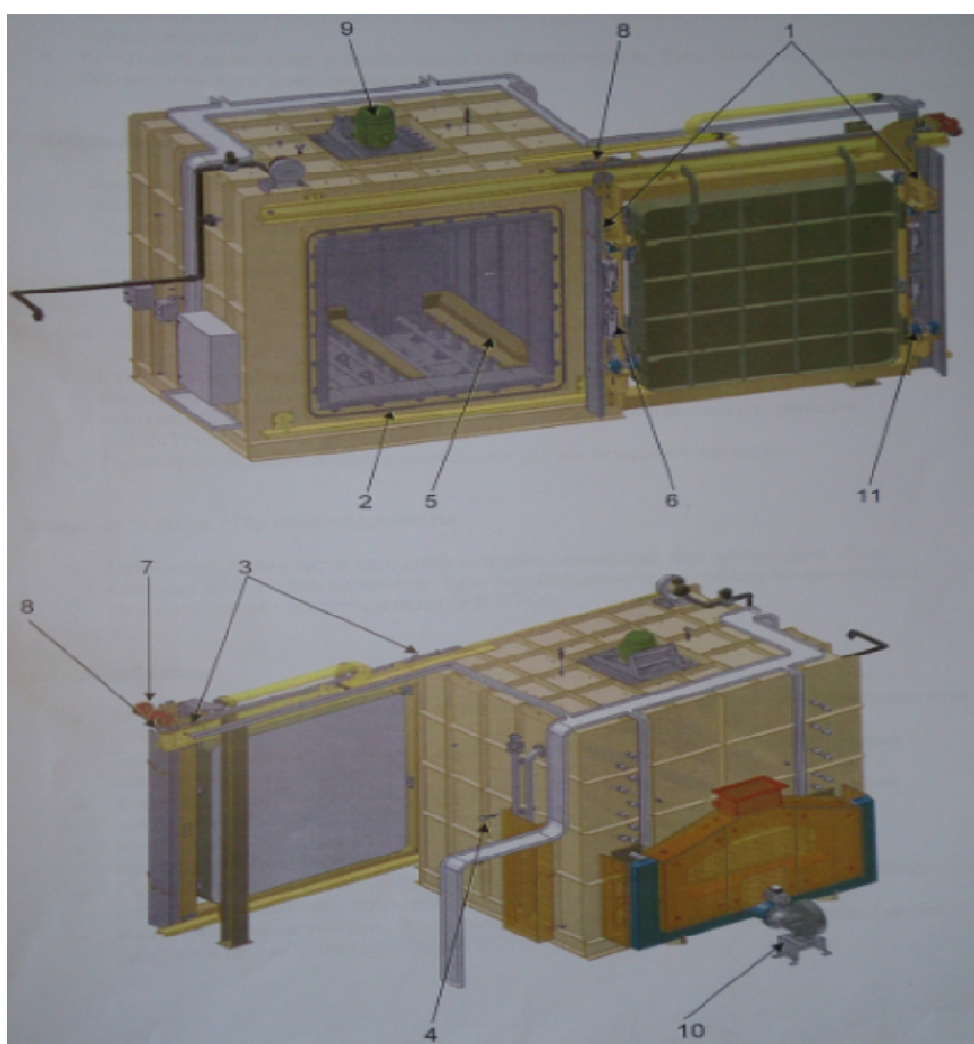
1 – датчик присутствия; 2 – дверной уплотнитель; 3 – рычажной выключатель; 4 – термоэлемент; 5 – опорные направляющие; 6 – цилиндр; 7 – мотор-редуктор; 8 – зубчатое колесо; 9 – перемешивающий вентилятор; 10 – радиальный вентилятор; 11 – опорный подшипник
